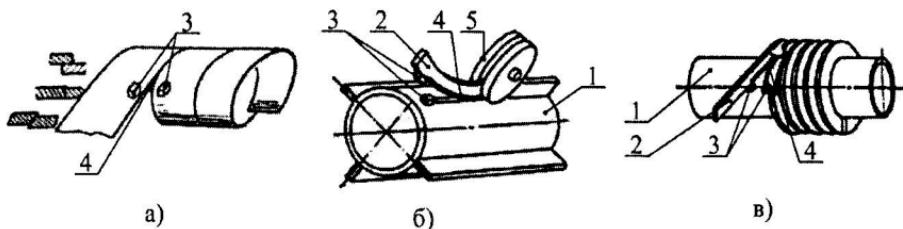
Схеми зварювання спіральношовних труб (а) і приварювання ребер (б, в): 1 – труба; 2 – ребро; 3 – контакти, 4 – зона формування шва, 5 – ролик
